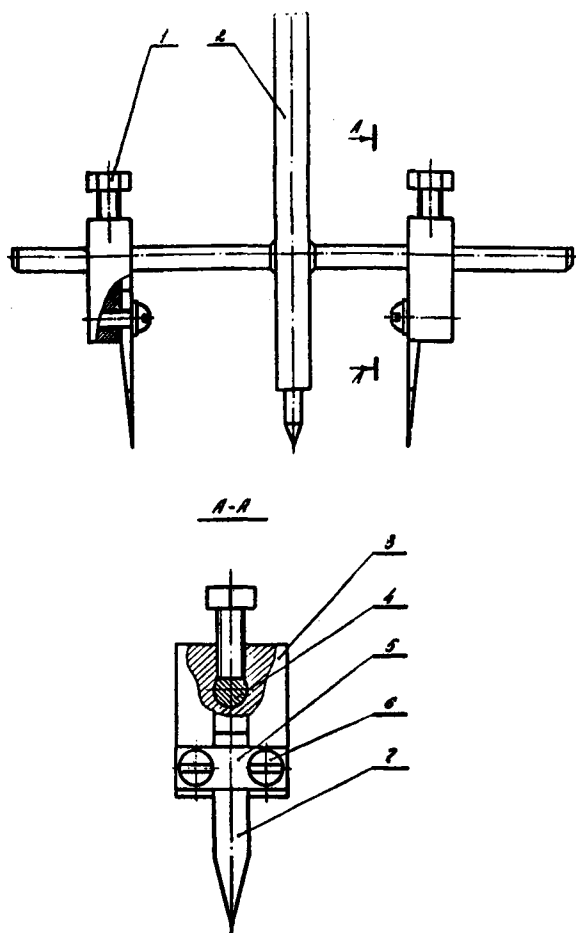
Приспособление для вырезки резиновых уплотнений:
